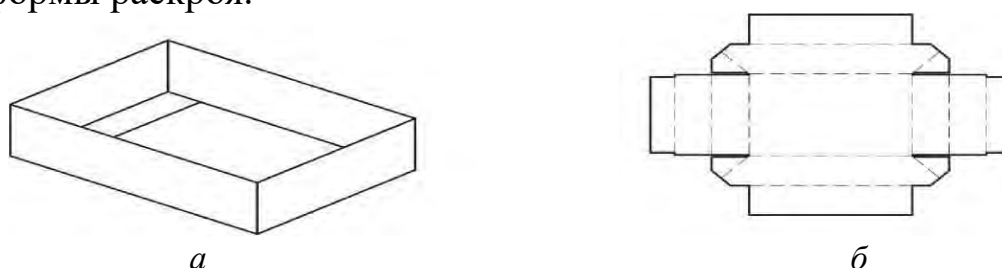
Внешний вид (а) и развертка (б) лотка с самозакрывающимися двойными стенками
